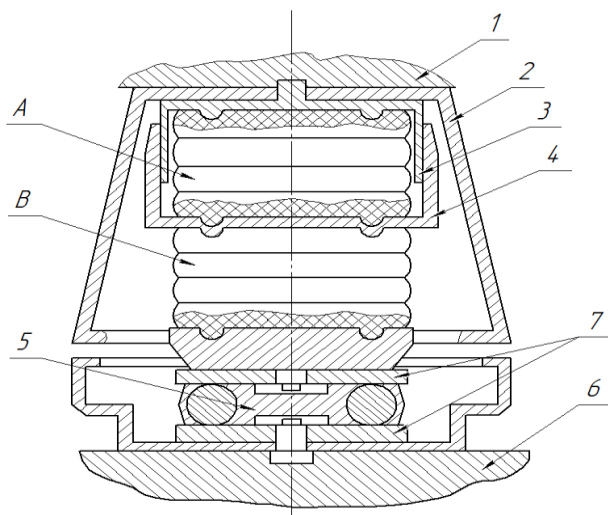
Конструктивная схема опорно-возвращающего устройства между кузовом и тележкой локомотива
